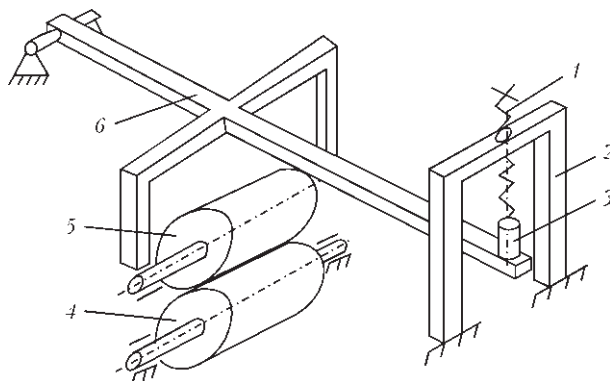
Кинематическая схема тянущей клетки: 1 — винт; 2 — неподвижная опора; 3 — датчик давления; 4 — неподвижный валок; 5 — верхний подвижный валок; 6 — рычаг; 7 — ось
